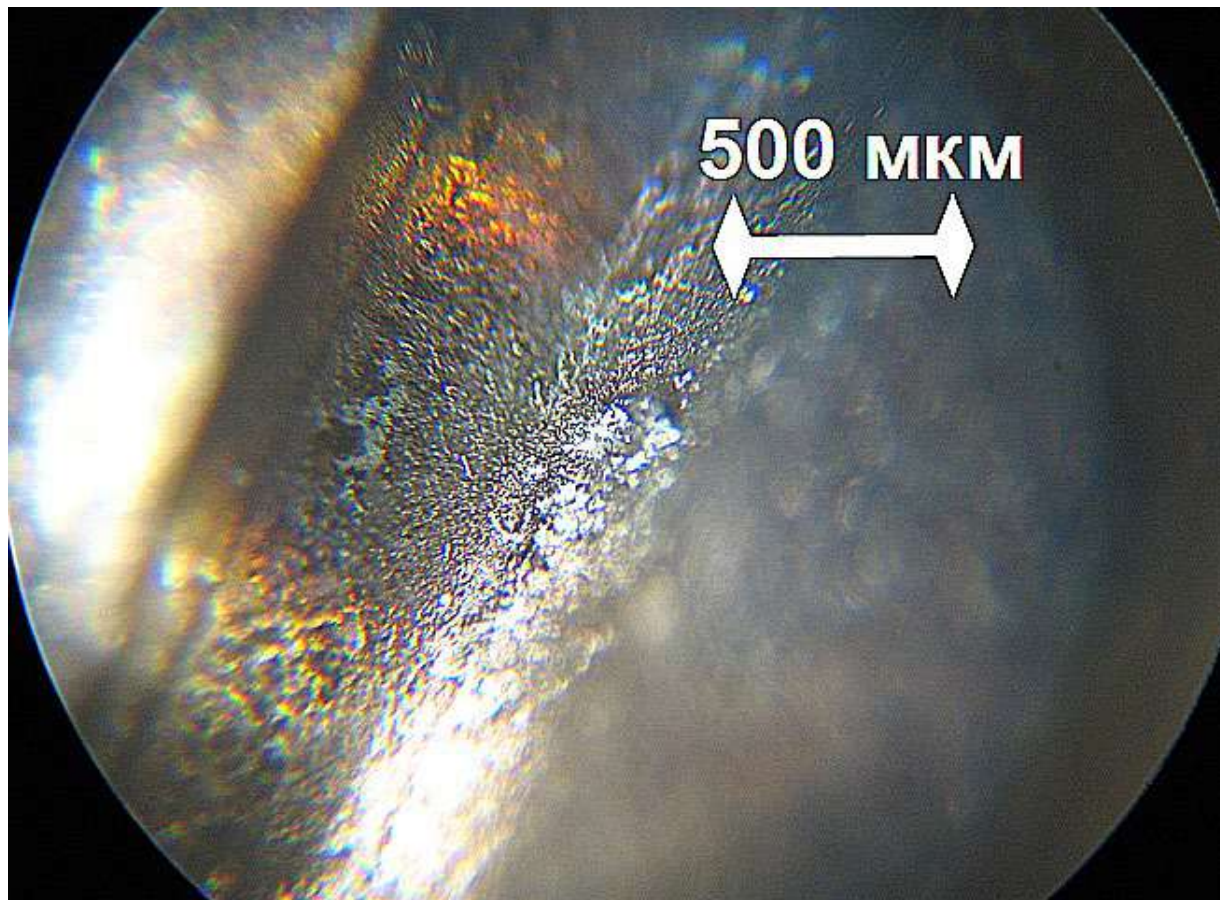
Признаки поверхностного проявления коррозии в области дна концентратора напряжений – канавки для подачи масла
